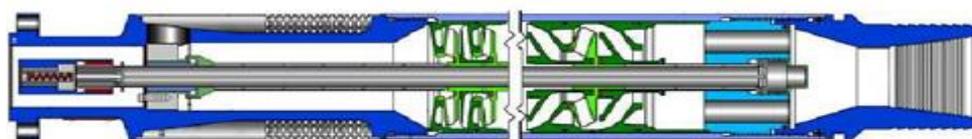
Центробежный газосепаратор фирмы Centrilift
